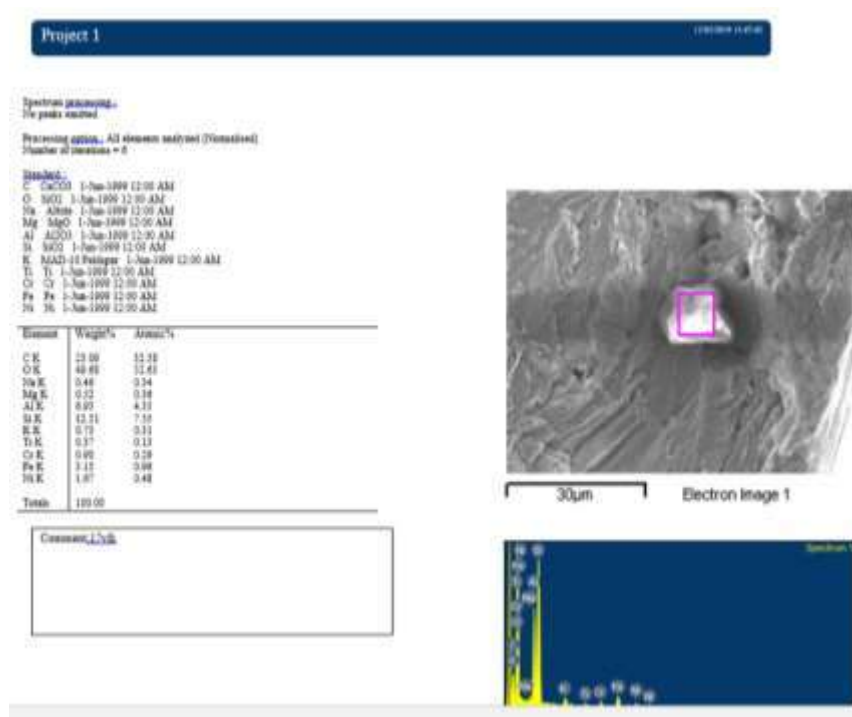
EDS de la superficie de fractura del I-718 a 667 MPa con pre-corrosión
